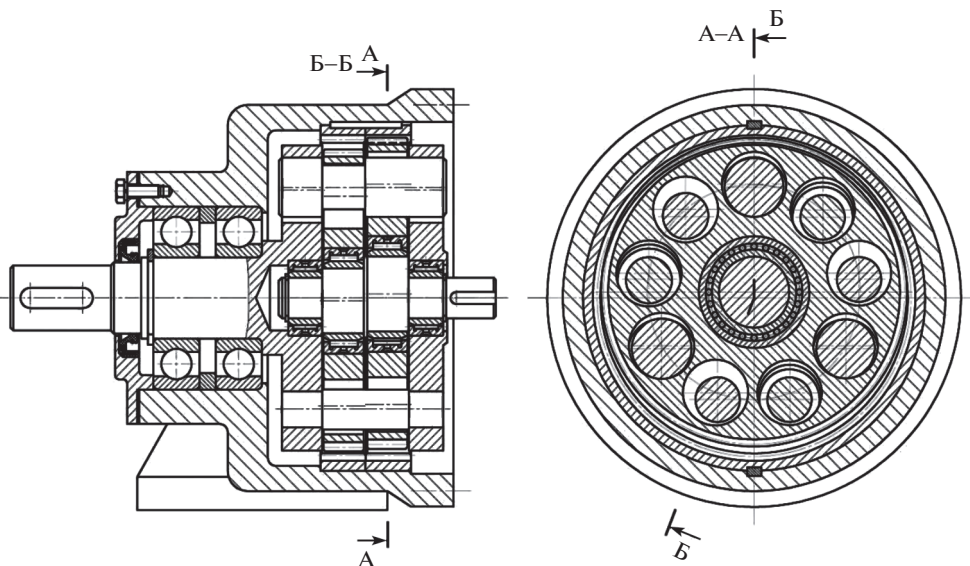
Планетарная передача с внутренними зацеплениями колес и малой разницей чисел их зубьев (пат. на изобр. РФ № 2460916).
